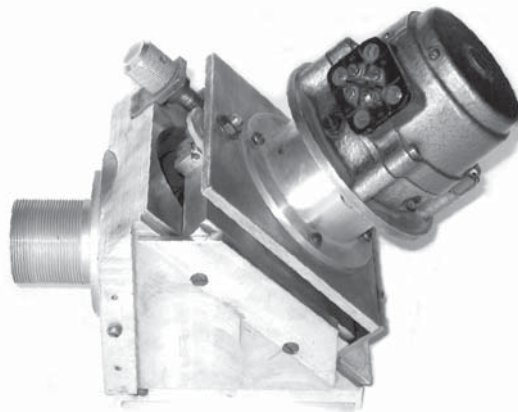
Общий вид оптического устройства для лазерной обработки материалов на основе динамического фокусатора
